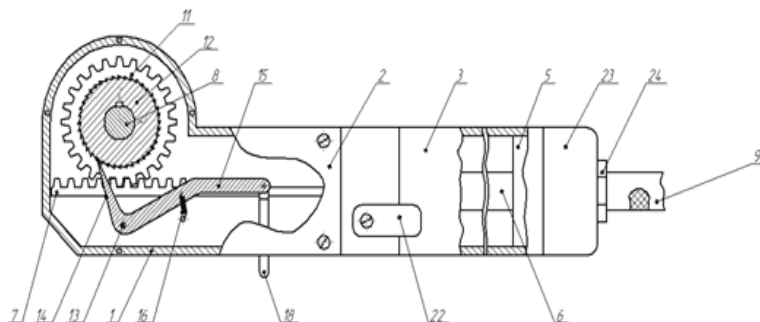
Схема гайковерта с реечно-зубчатой передачей
